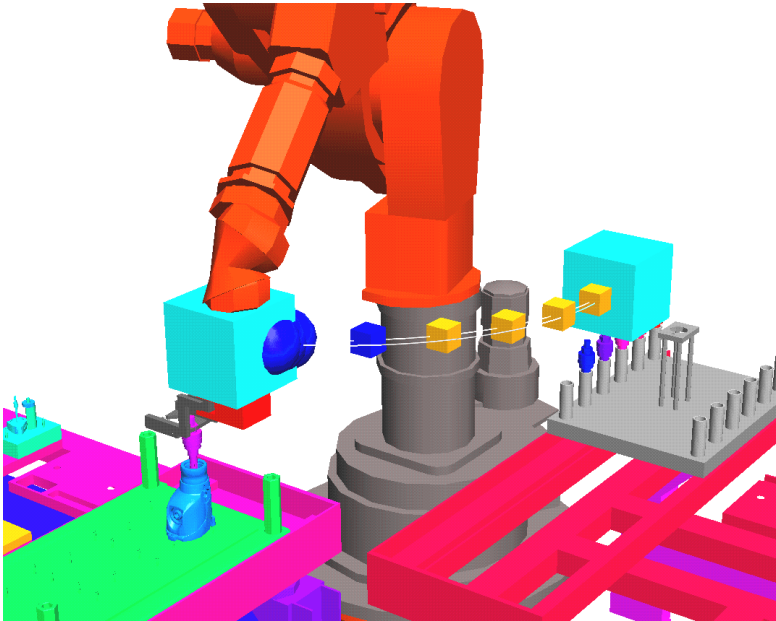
Einsatz der Bahnplanung zur Generierung kollisionsfreier Montageprozesse
